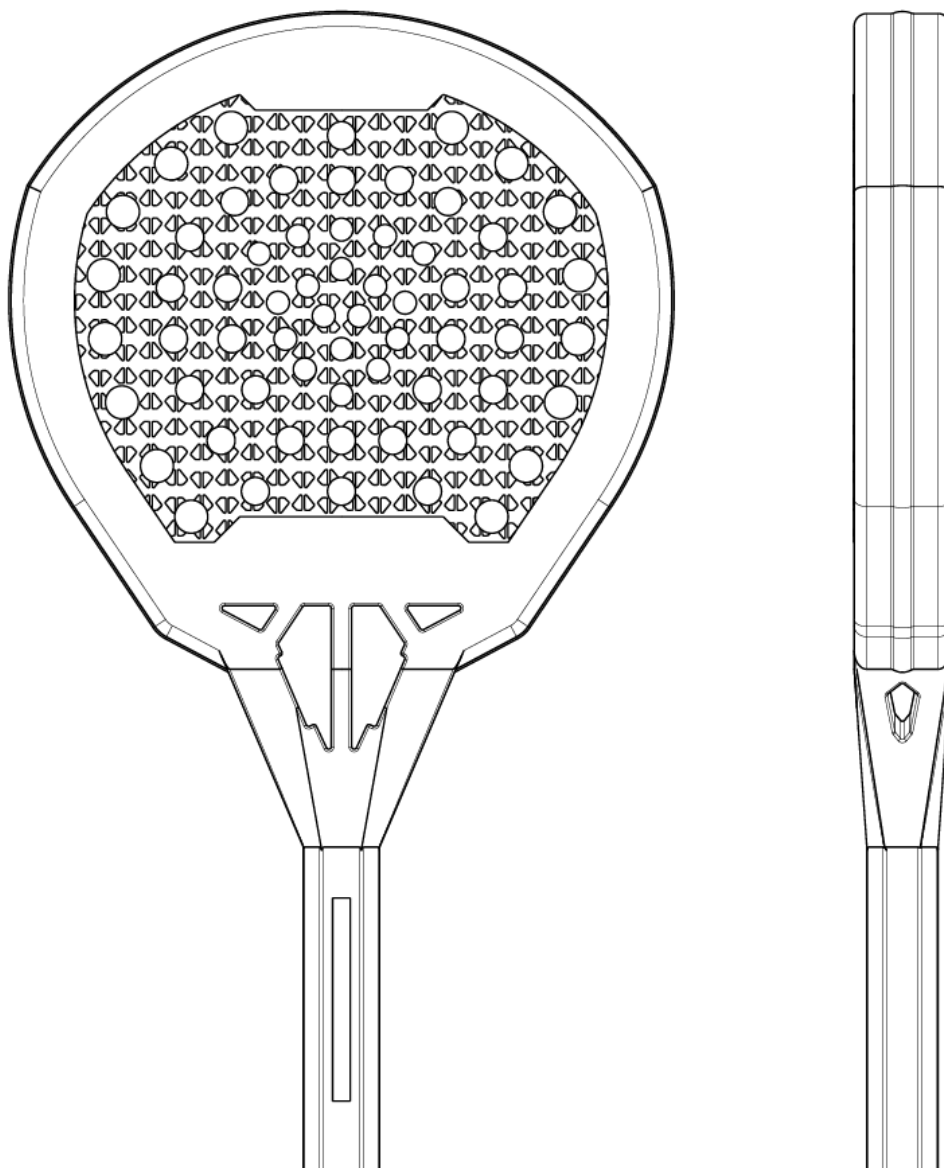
Alzado y Perfil del diseño propuesto para la pala de pádel.
